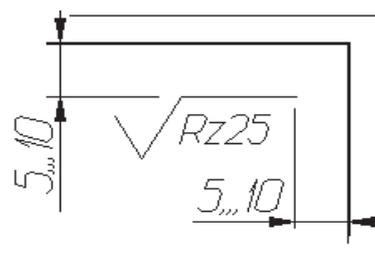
Указание шероховатости одинаковой для всех поверхностей изделия
